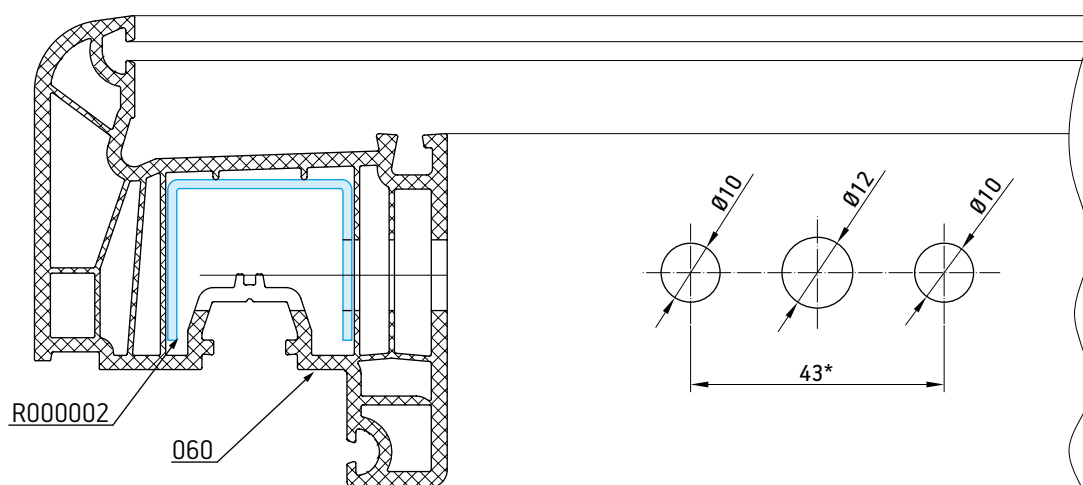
Фрезеровка и сверление отверстий для установки фурнитуры
